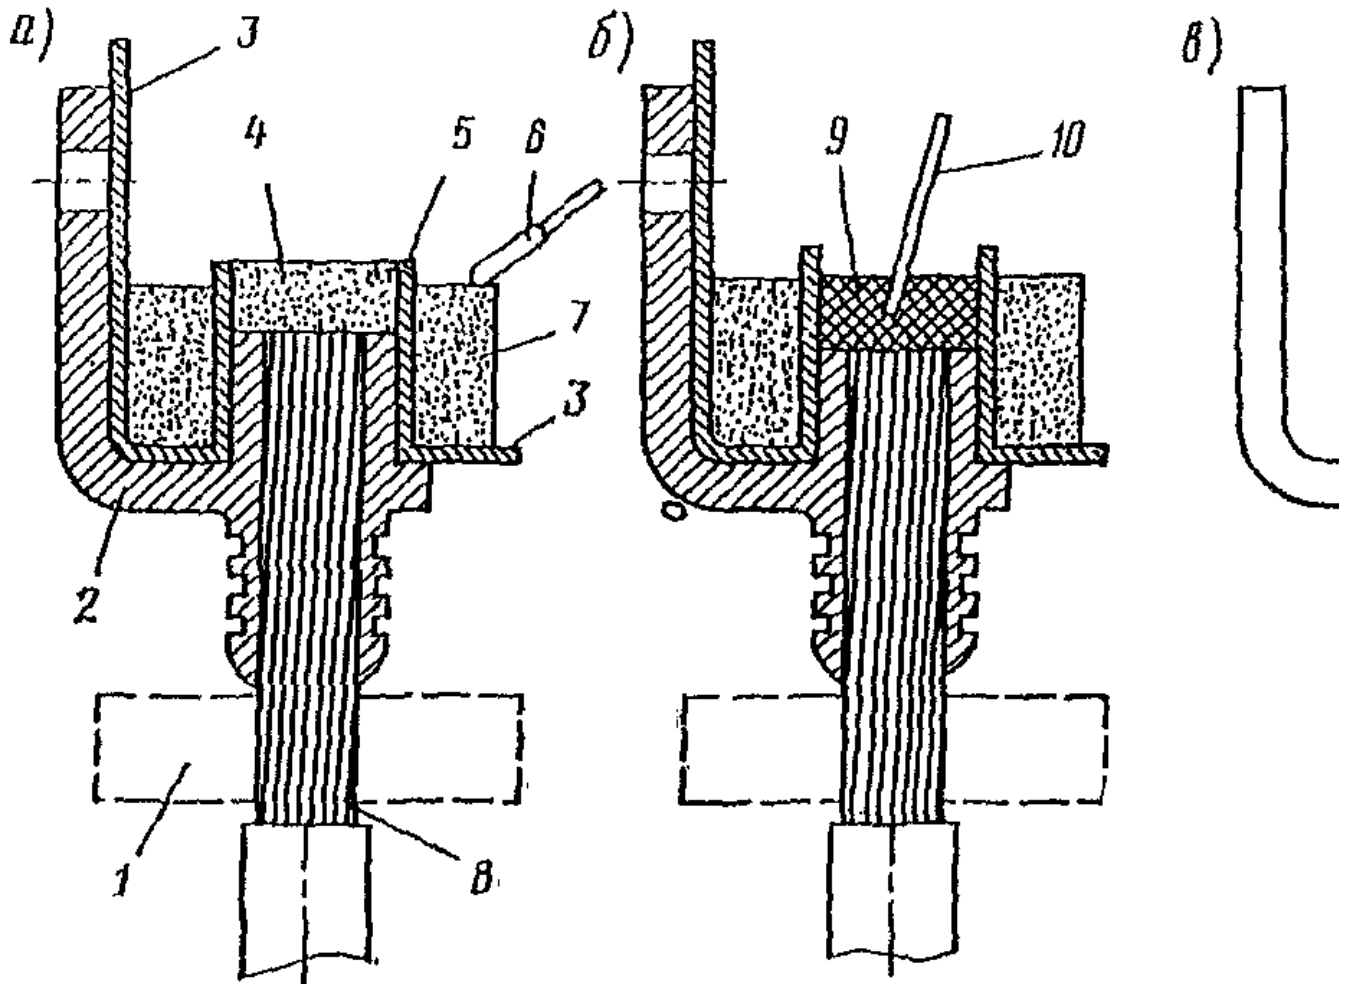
Приварка кабельного наконечника типа ЛАШ: а - наконечник, подготовленный к сварке; б - перемешивание плавки; в - наконечник после окончания сварки и зачистки неровностей напильником; 1 - охладитель; 2 - наконечник; 3 - экраны; 4 - присадочный материал; 5 - кокиль; 6 - термитная спичка; 7 - муфта термитного патрона; 8 - жила кабеля; 9 - сварочная ванна; 10 - проволочная мешалка
